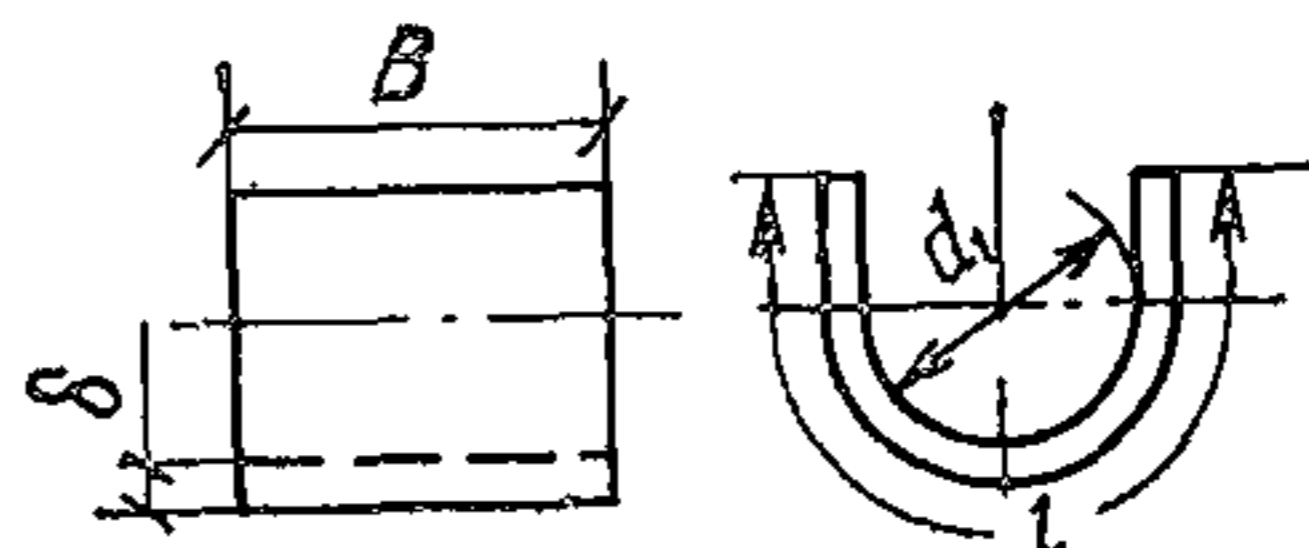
Конструкция и размеры стальных скоб-подкладок
